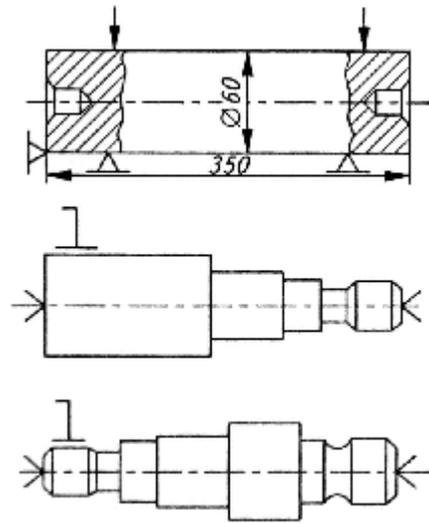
Черновое и чистовое базирование при изготовлении вала из проката
